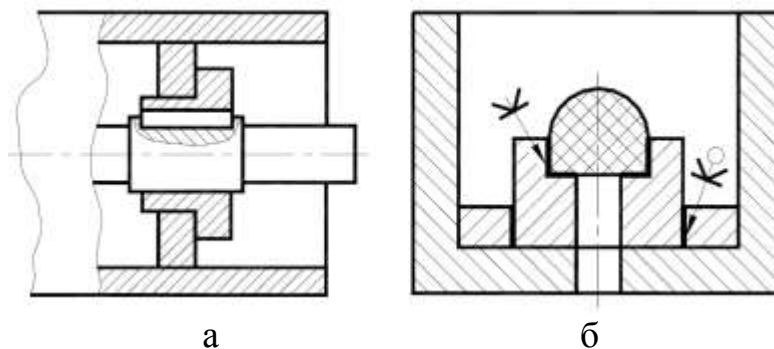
Изображения сварного (а) и клееного (б) соединений в сборе с другими изделиями на чертежах общего вида
